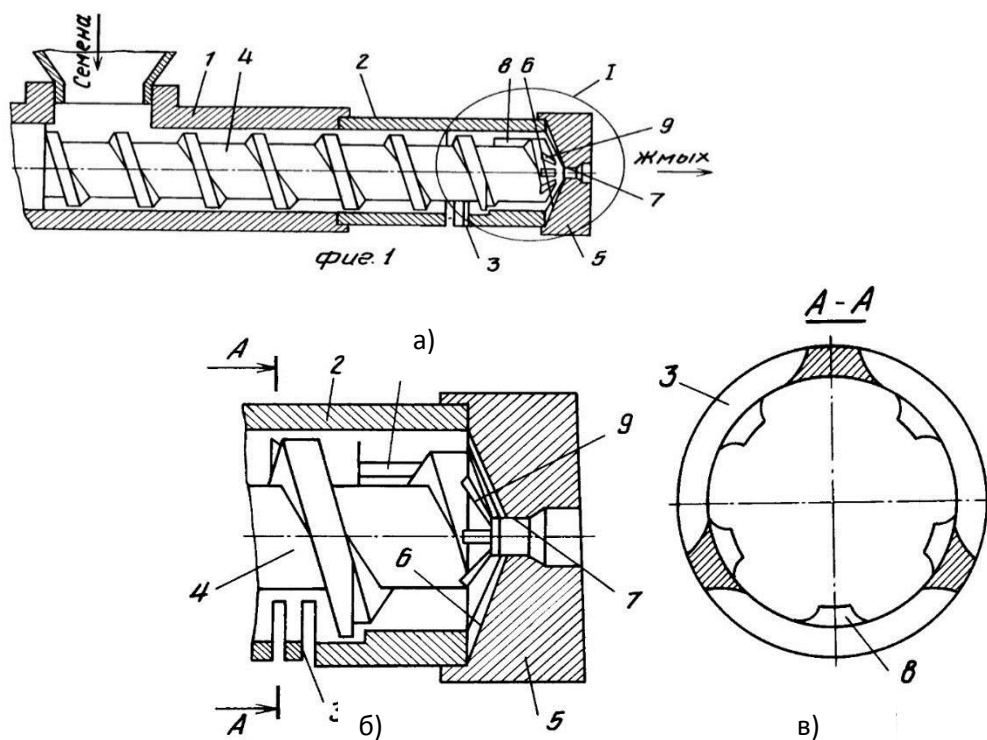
Масловыжимной пресс а) – общий вид; б) – узел дополнительного перемалывания жмыха; в) – зерный цилиндр.
